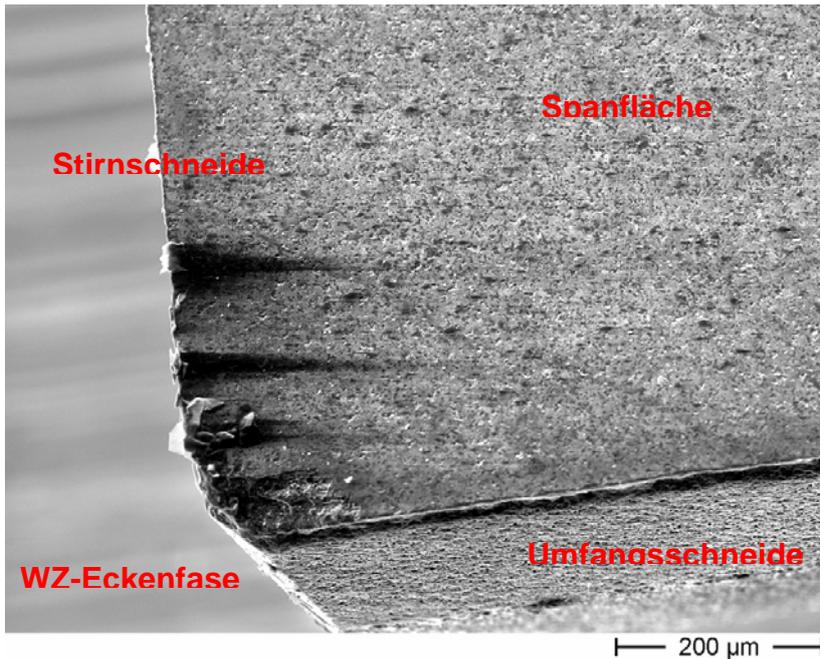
Werkzeugecke eines PKD-Schaftfräasers
